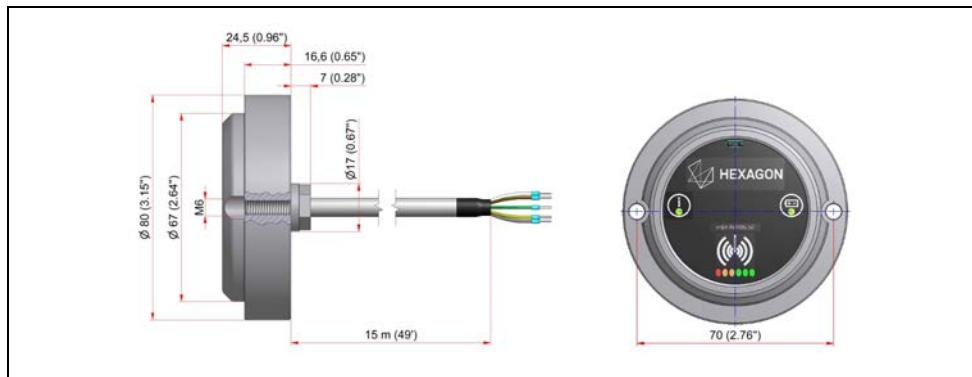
Abmessungen RWR95.50-A (Kabelabgang axial)
